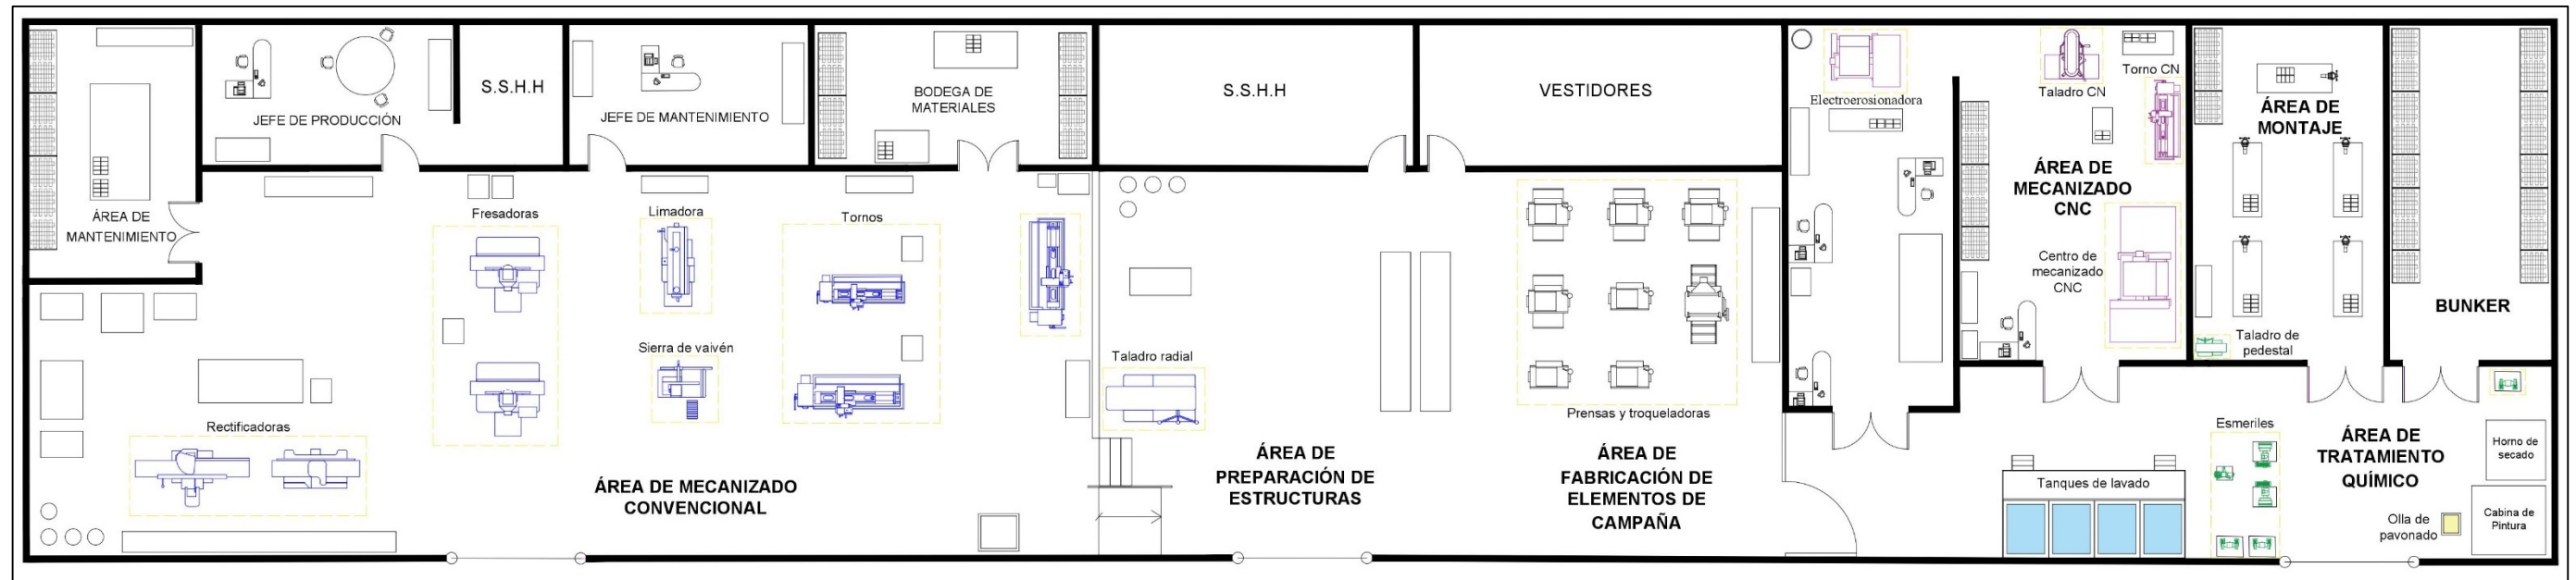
Layout actual de la planta de fabricación en Santa Bárbara EP
